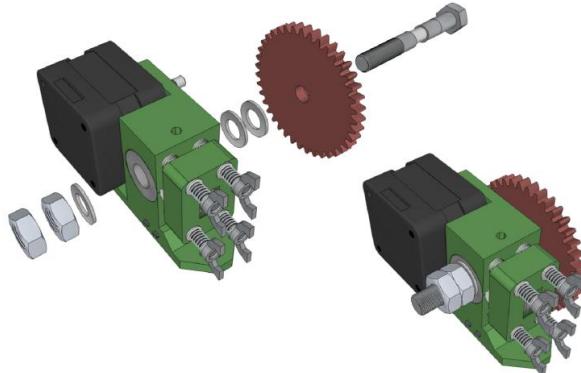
Colocación Montaje del motor y ensamblado de los engranajes (paso 5)
